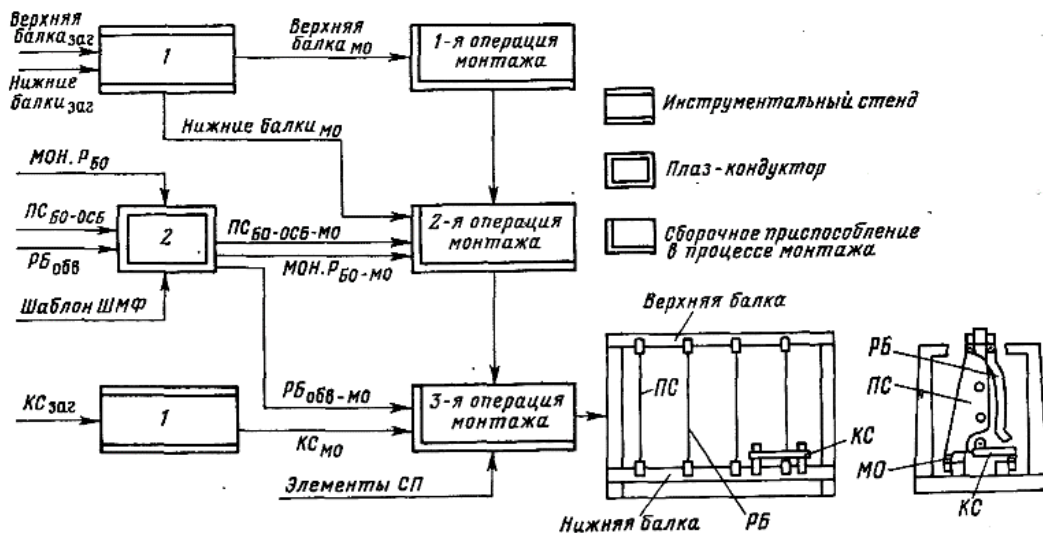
Схема монтажа приспособления с использованием плаз-кондуктора и инструментального стенда
